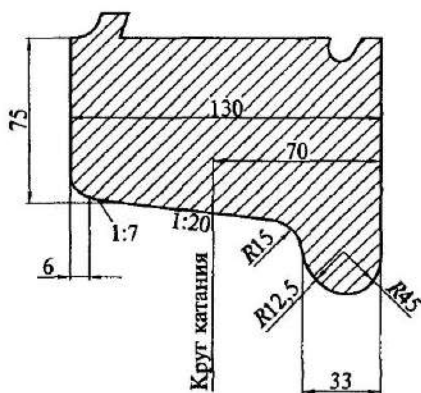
Профиль бандажа и поверхности катания колеса
